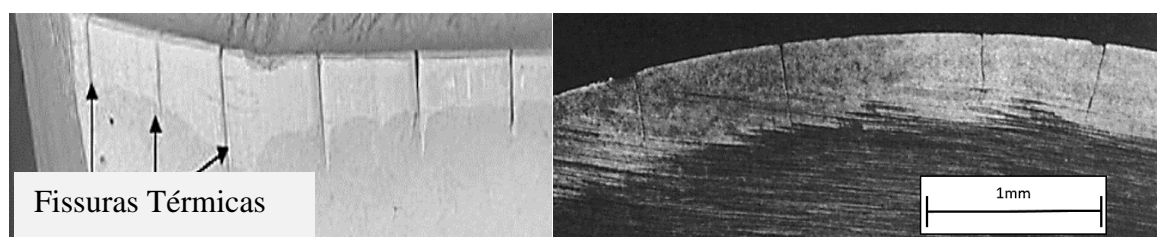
Fissuras de origem térmica, transversais na direção normal à aresta de corte (Machado et al., 2009)
